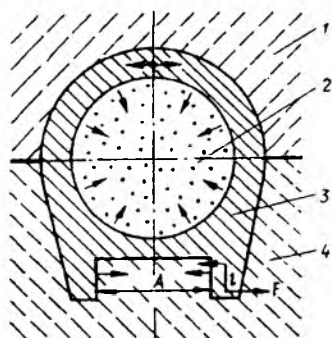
Напряжение в отливке и форме: 1 – верхняя полуформа; 2 – стержень; 3 – отливка; 4 – нижняя полуформа
